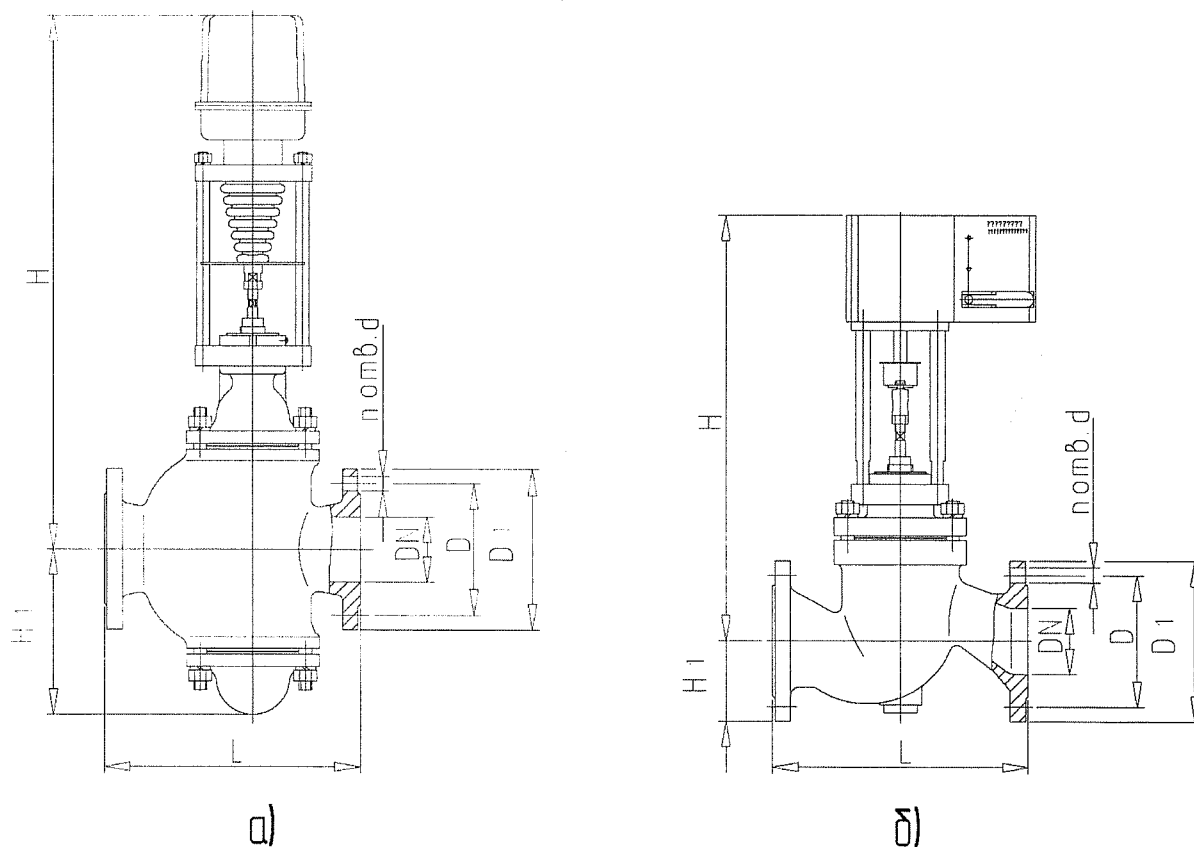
а) Клапан регулирующий двухседельный фланцевый, б) клапан запорный и запорно-регулирующий односедельный фланцевый.
